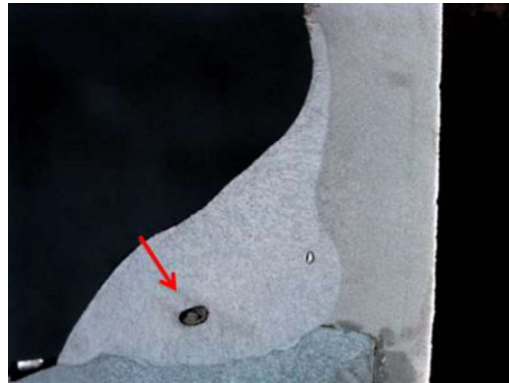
6 – Porosidade num canto de soldadura (Hadzihafizovic, 2022).
